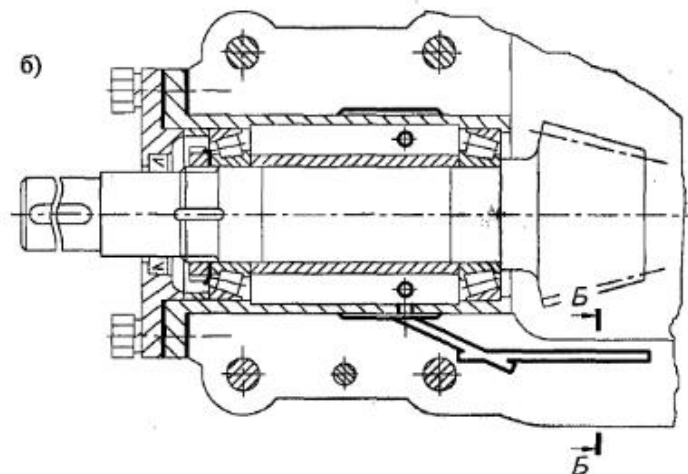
Конструктивные решения по смазыванию подшипников и зубчатых колес редукторов:
